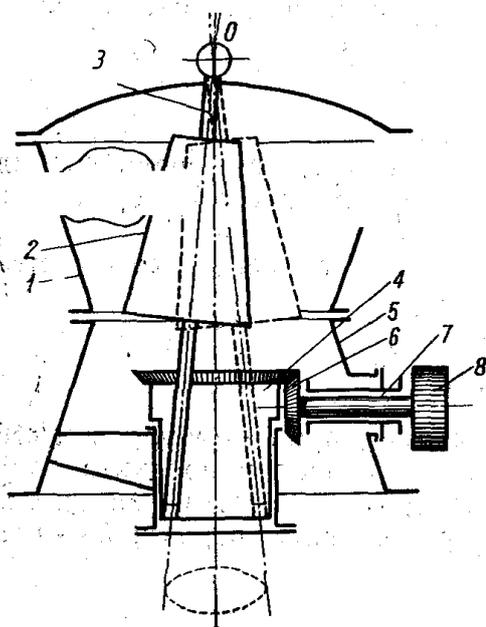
Схема конусной дробилки для крупного дробления с подвешенным валом: 1 — верхняя часть станины (неподвижная коническая чаша); 2 — дробящий конус; 3 — вал; 4 — эксцентриковый стакан; 5 — нижняя часть станины; 6 — коническая передача; 7 — приводной вал; 8 — шкив
